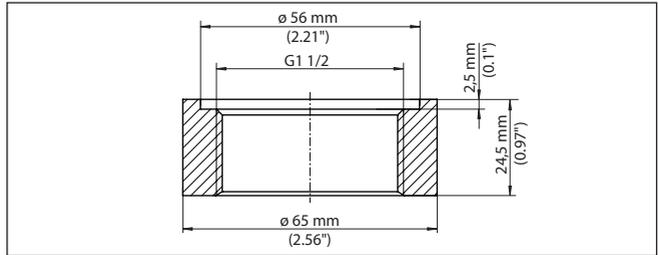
Dimensions raccord à souder filetage G1½ (DIN 3852-A) - VEGABAR 82, 83, 86, 87
